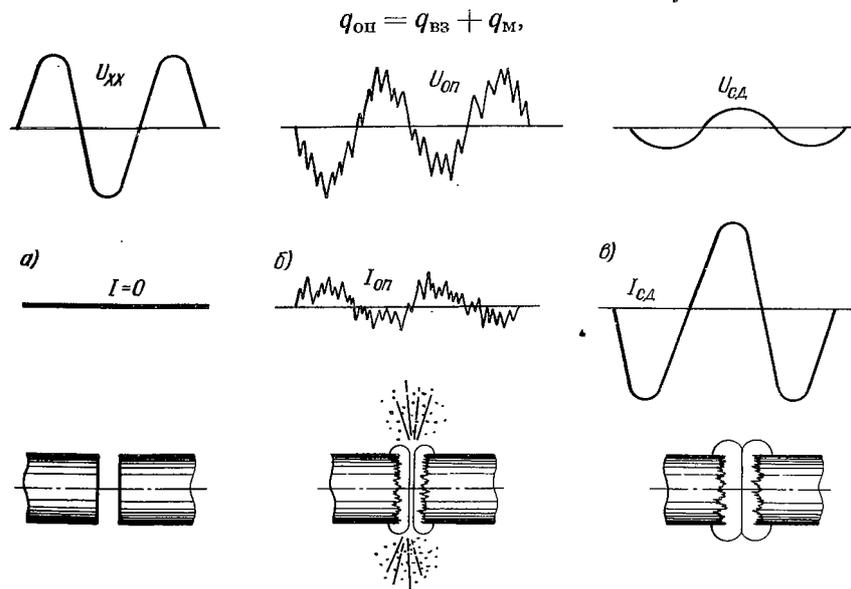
Осциллограмма процесса стыковой сварки оплавлением
